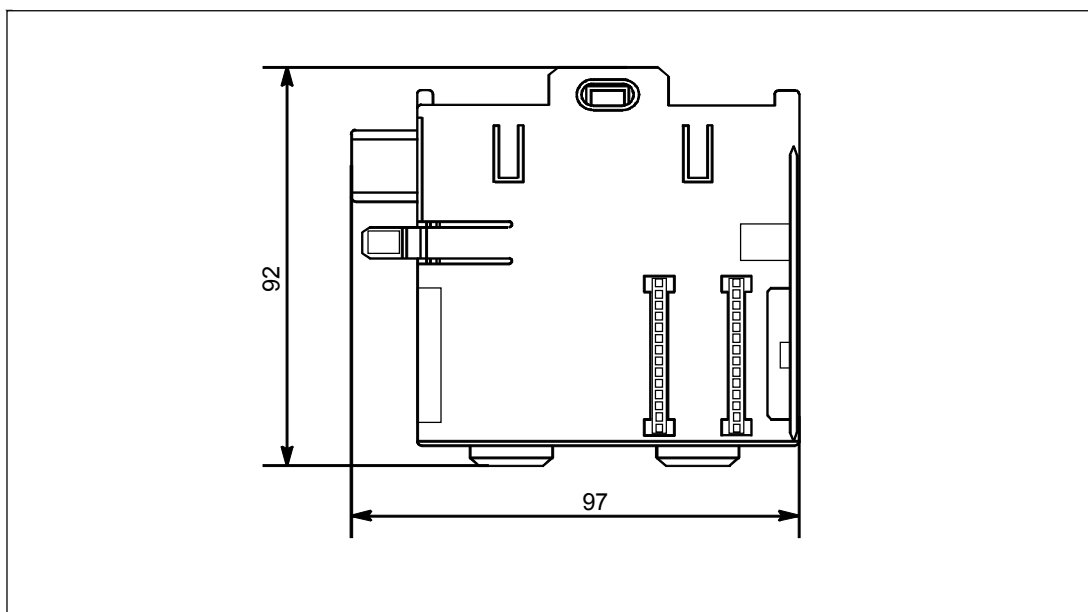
Чертеж с размерами шинного модуля для разделительного модуля
